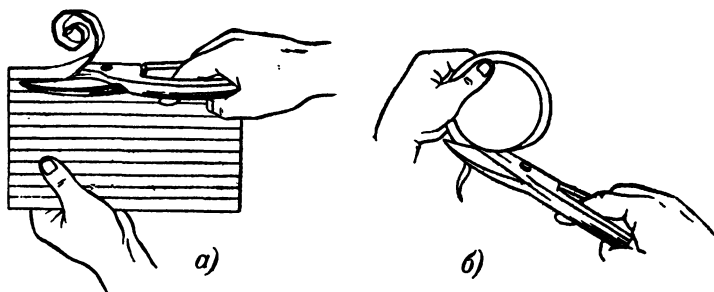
Резка деталей из листового материала слесарными ножницами, а — резка полос; б — изготовление круга.
